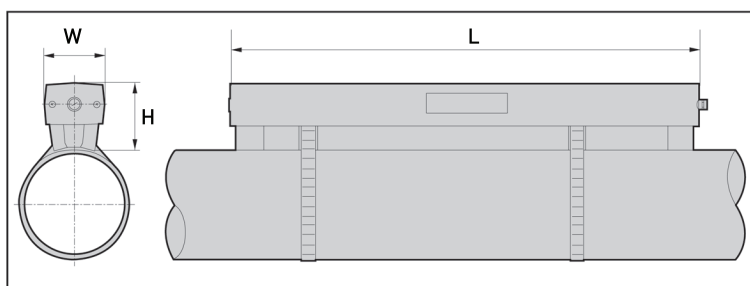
Dimensões do sensor tipo "clamp-on"
